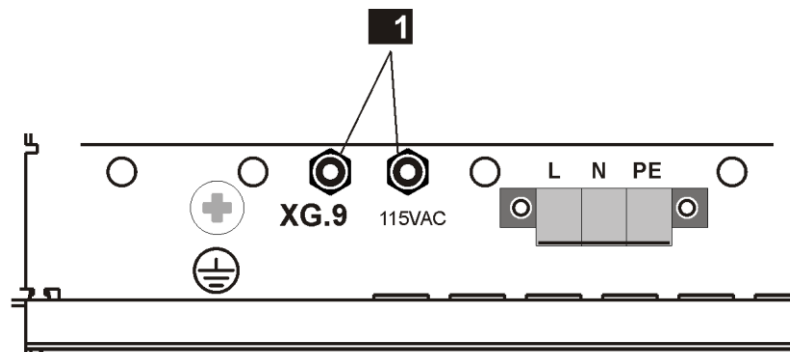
Rückansicht des Baugruppenträgers M 3421 mit Klemmen
